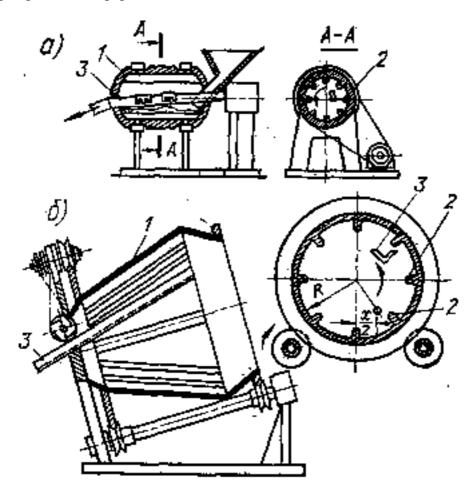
Бункерные загрузочныеприспособления с барабаном:
